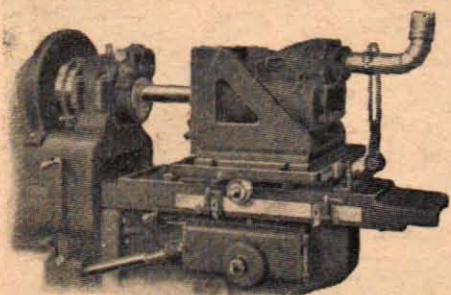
Cylinderslipning i motorblock. Slipdammet suges ut genom röret till höger.
